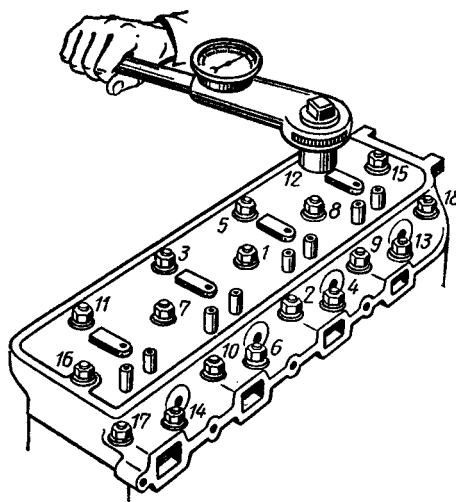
Последовательность затяжки (указана цифрами) гаек крепления головки цилиндров двигателя ГАЗ-53.
